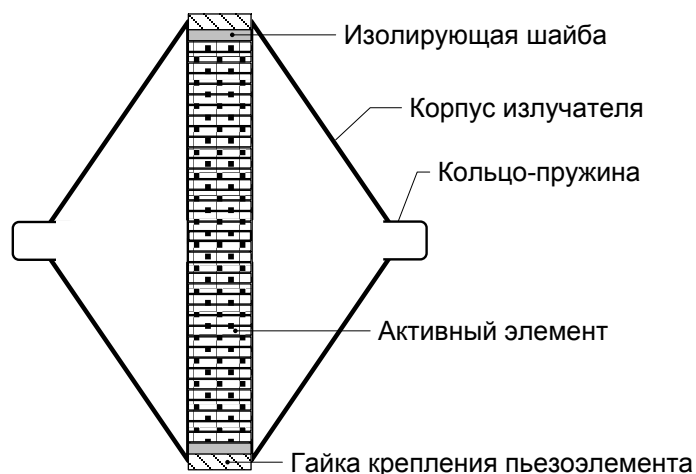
Конструкция НЧИ с биконической излучающей поверхностью.
